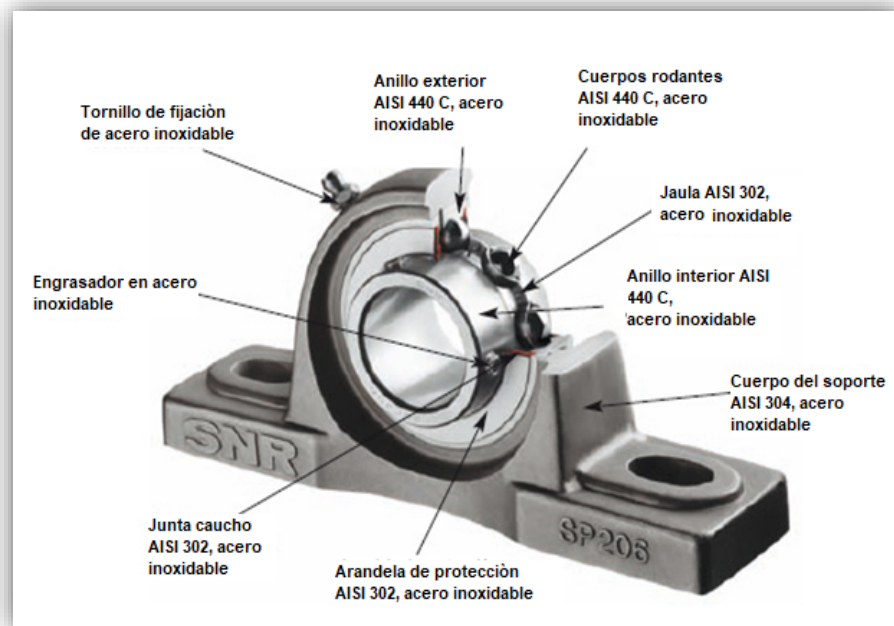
Partes de un rodamiento de motor eléctrico.
